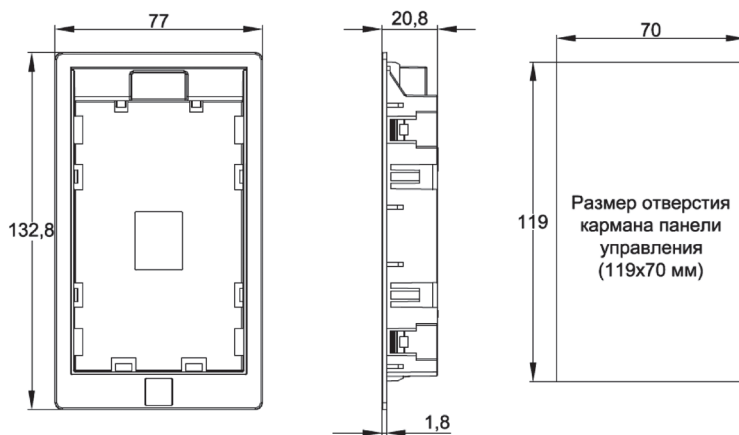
Габаритные размеры держателя внешней цифровой двухстрочной панели управления (единица измерения – мм)
